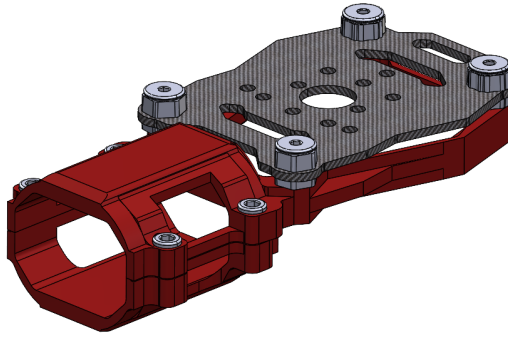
Soporte de sujeción del motor en vista isométrica. Fuente: Propia.
